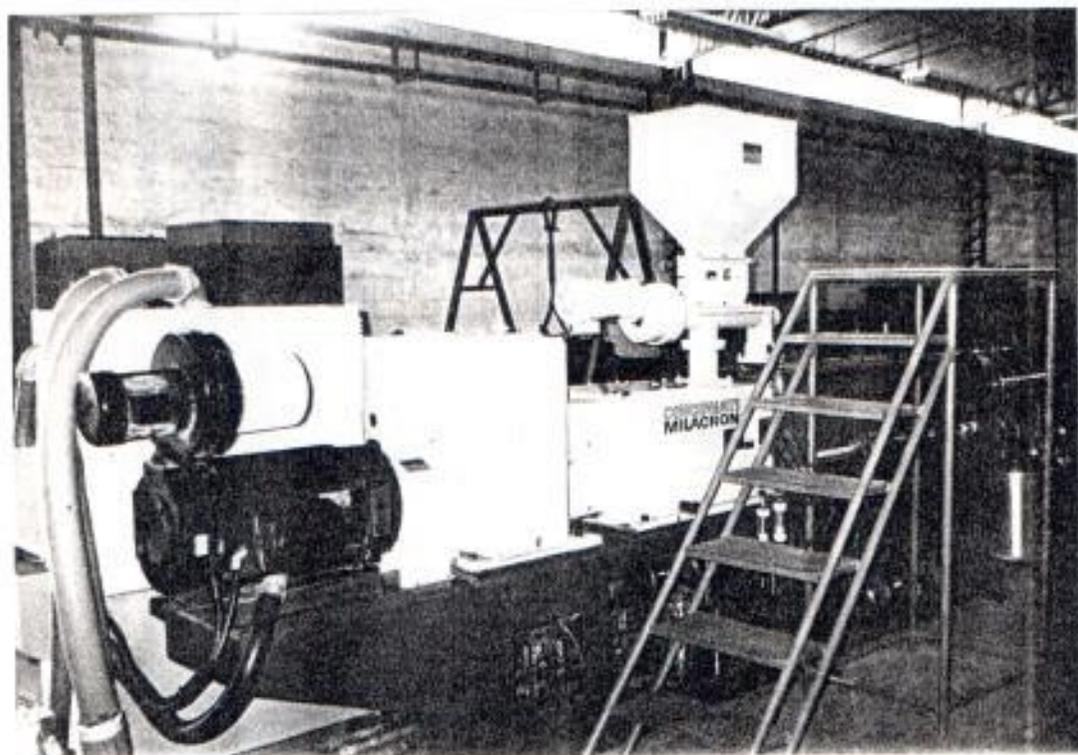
VISTA PRINCIPAL DEL MOTOR DE 75 HP.
